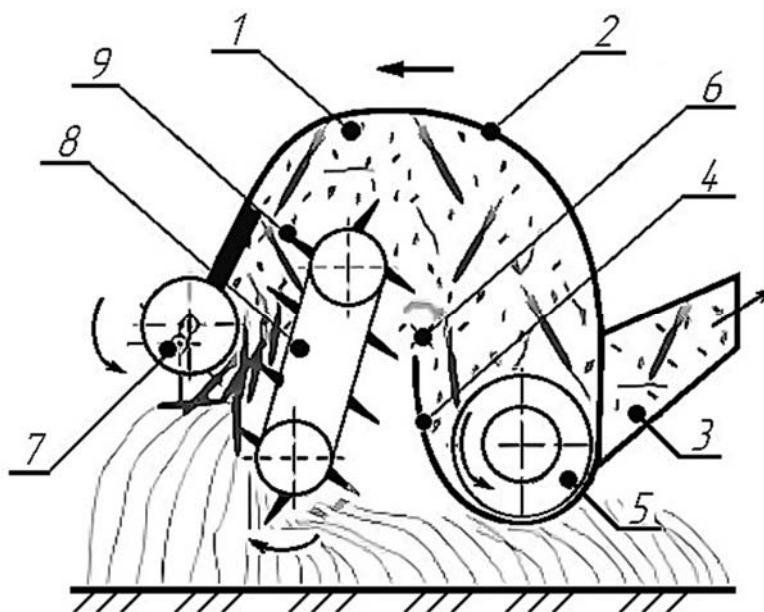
Схема очесывающей жатки транспортерного типа: 1 – корпус; 2 – крыша; 3 – наклонная камера; 4 – сборная камера; 5 – шнек; 6 – битер; 7 – питатель; 8 – очесыватель; 9 – зубья
